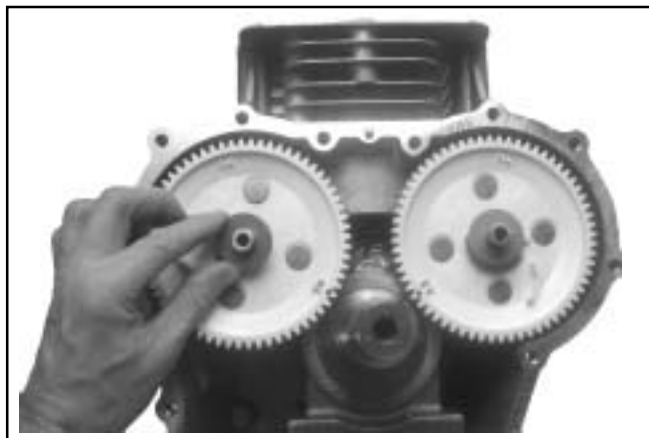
Instalación del engranaje de leva de admisión y la arandela de empuje.
